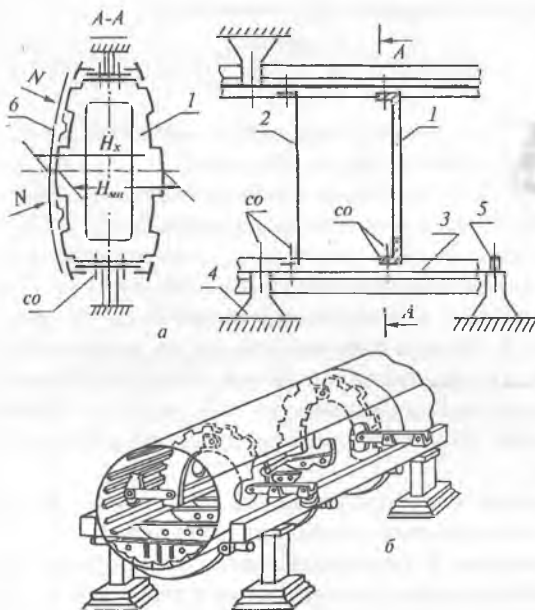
Сборка по внутренней поверхности обшивки:
